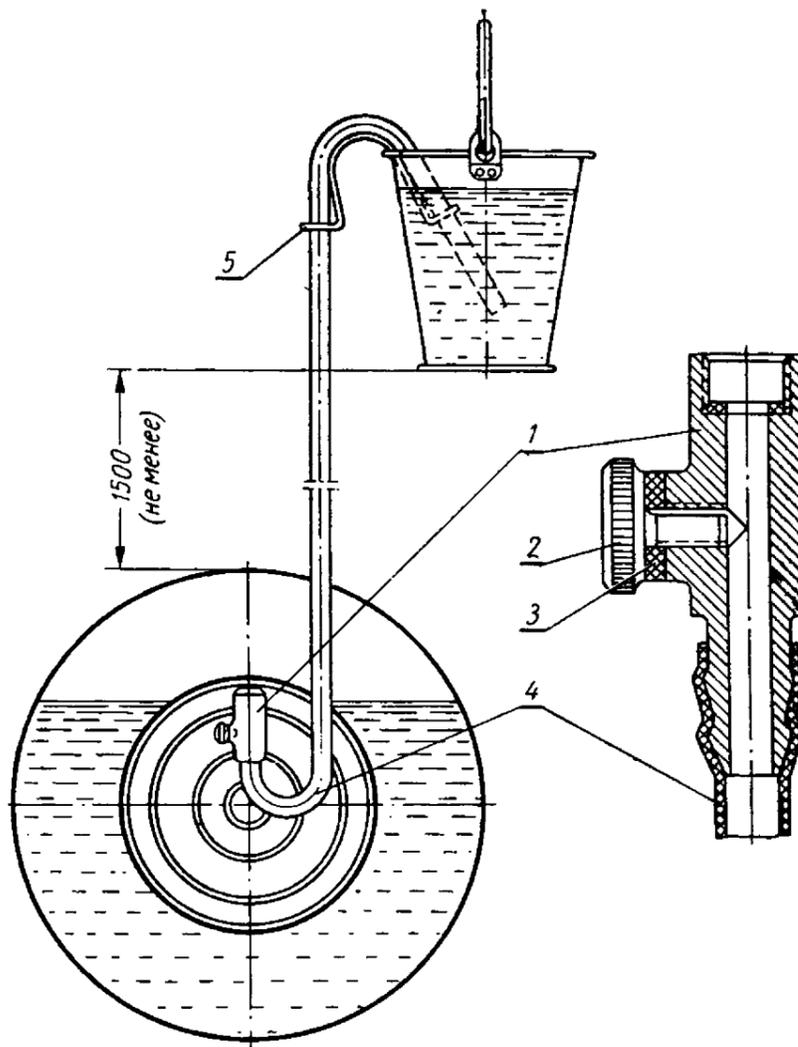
Приспособление для заливки воды в камеры задних колес:
